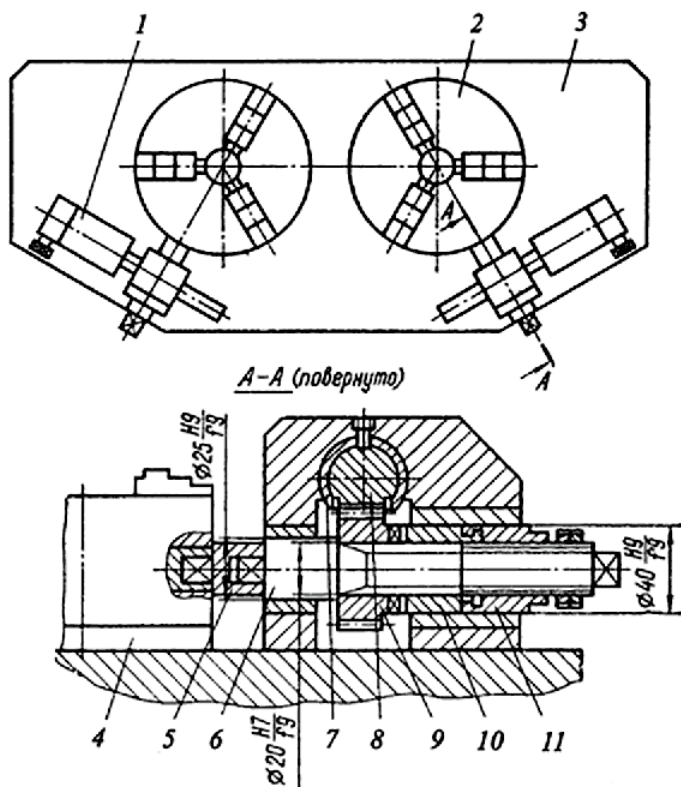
Приспособление для обработки отверстий в деталях типа крышек, фланцев, дисков и др.
